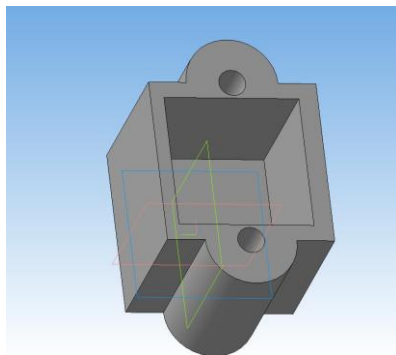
Эскиз детали с определением сквозных отверстий
